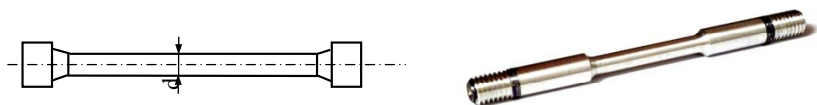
Схема и общий вид образцов для испытаний на растяжение
